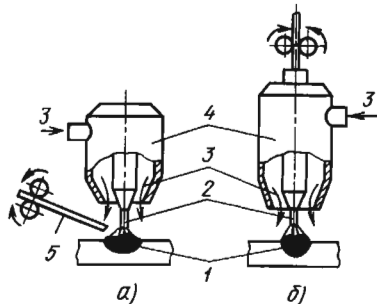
Схемы сварки неплавящимся (а) и плавящимся (б) электродами в защитных газах: 1 — металл шва; 2 — электрод; 3 — защитный газ; 4 — сопло горелки; 5 — присадочная проволока
